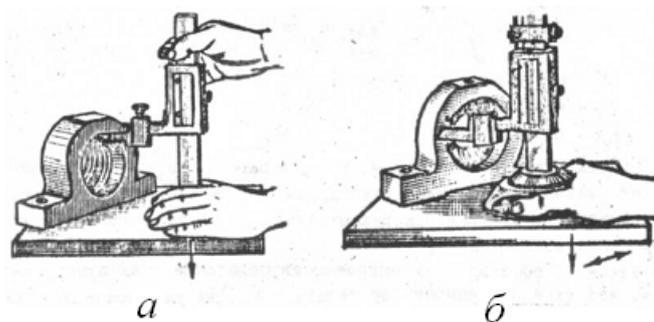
Измерение и разметка штангенрейсмусом:
